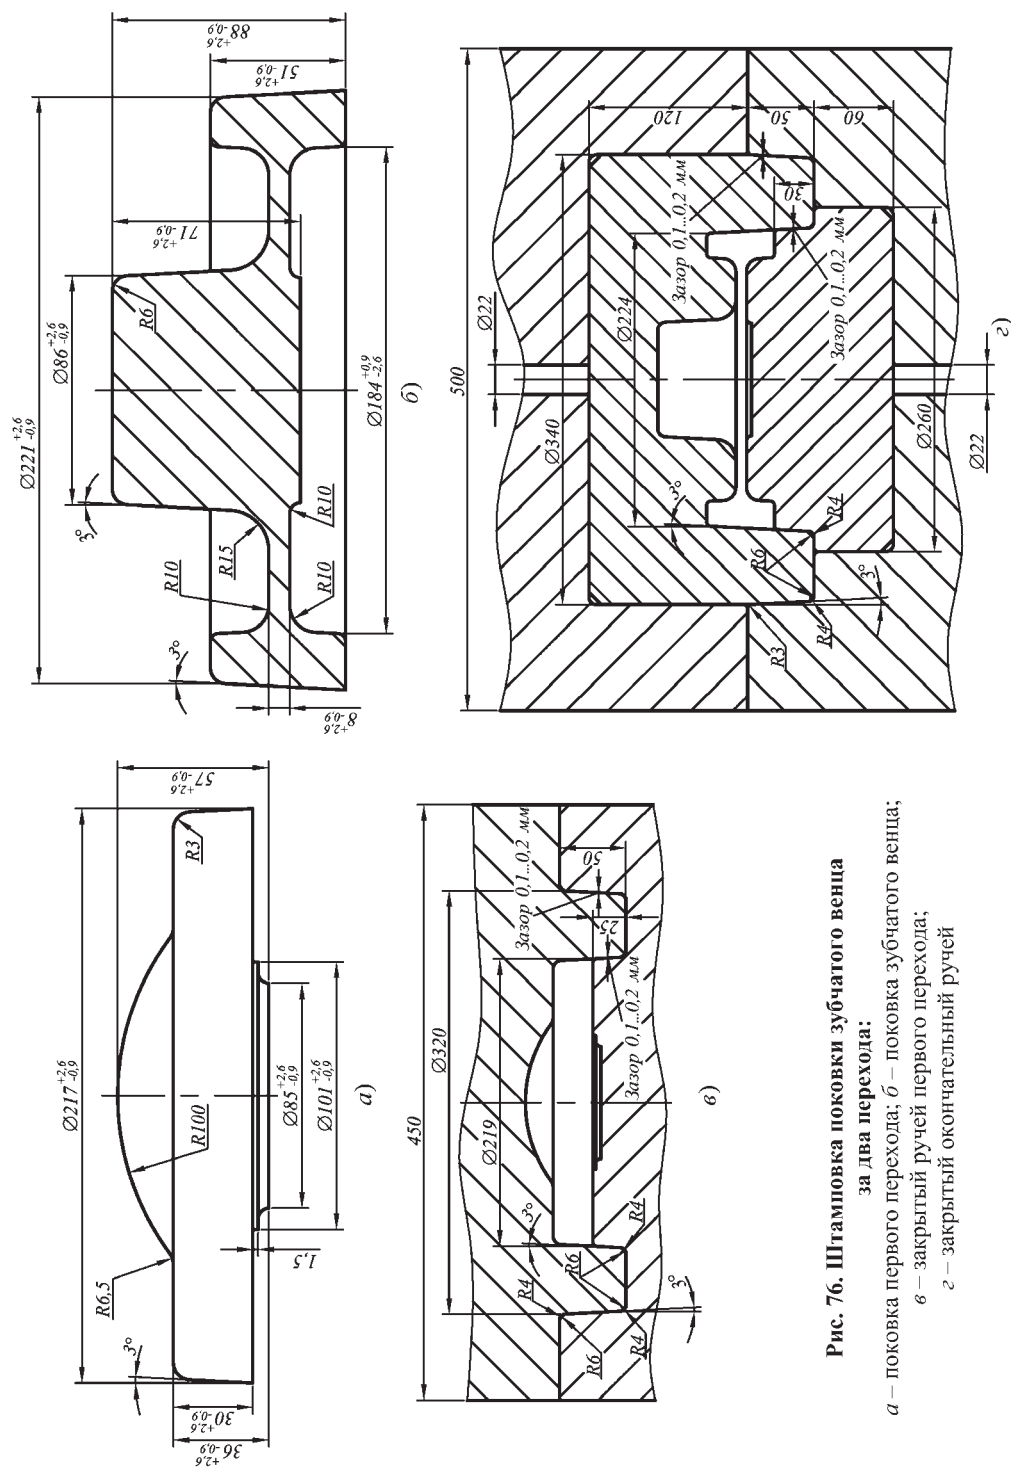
Штамповка поковки зубчатого венца за два перехода:
